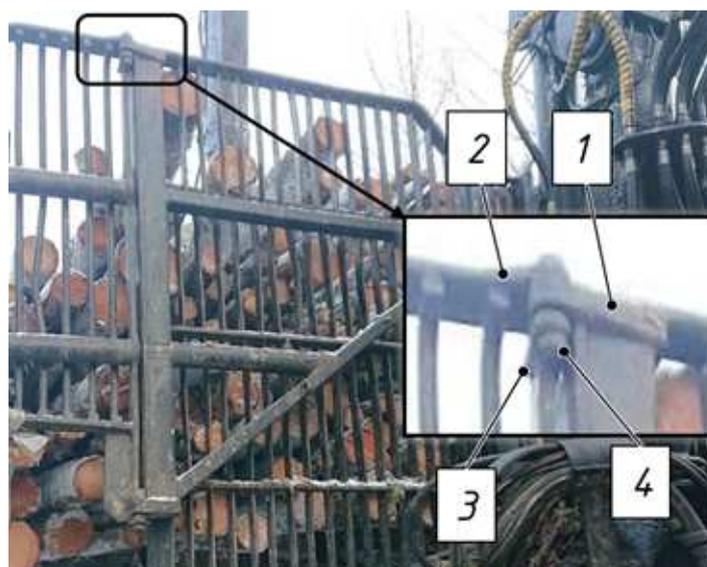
Защитный экран форвардера Rottne с поворотными боковыми экранами
